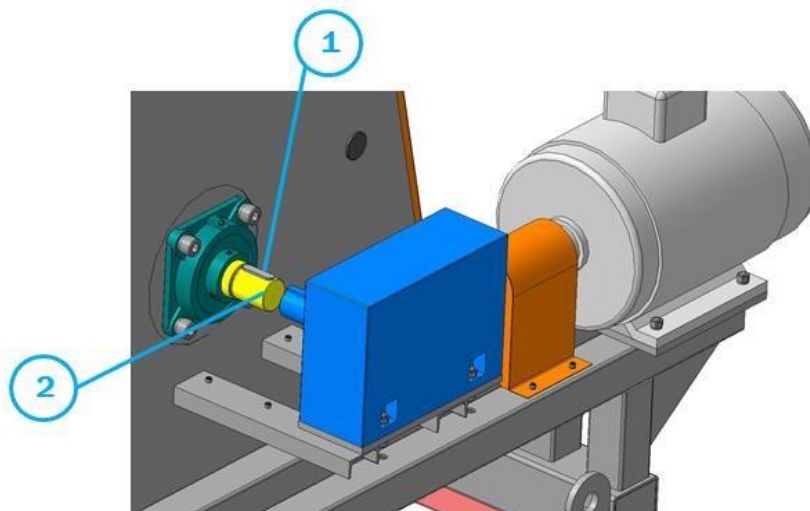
Схема демонтажа корпусного подшипника задней опоры
